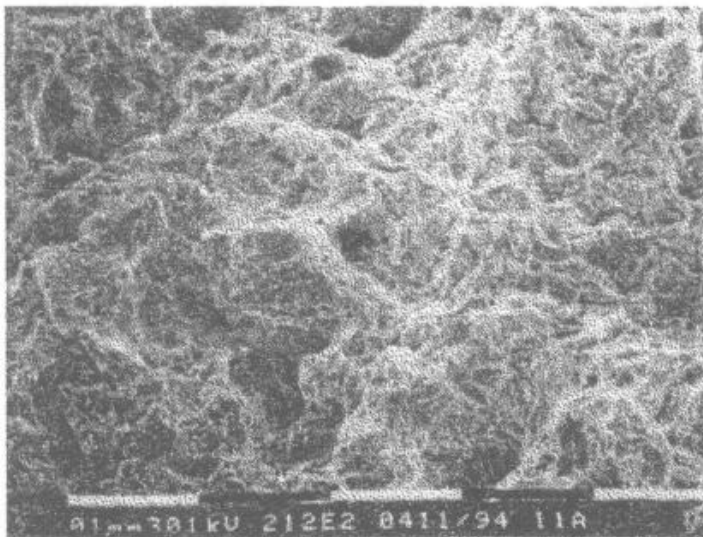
Aspetto tipico della zona rotta a strappo.
